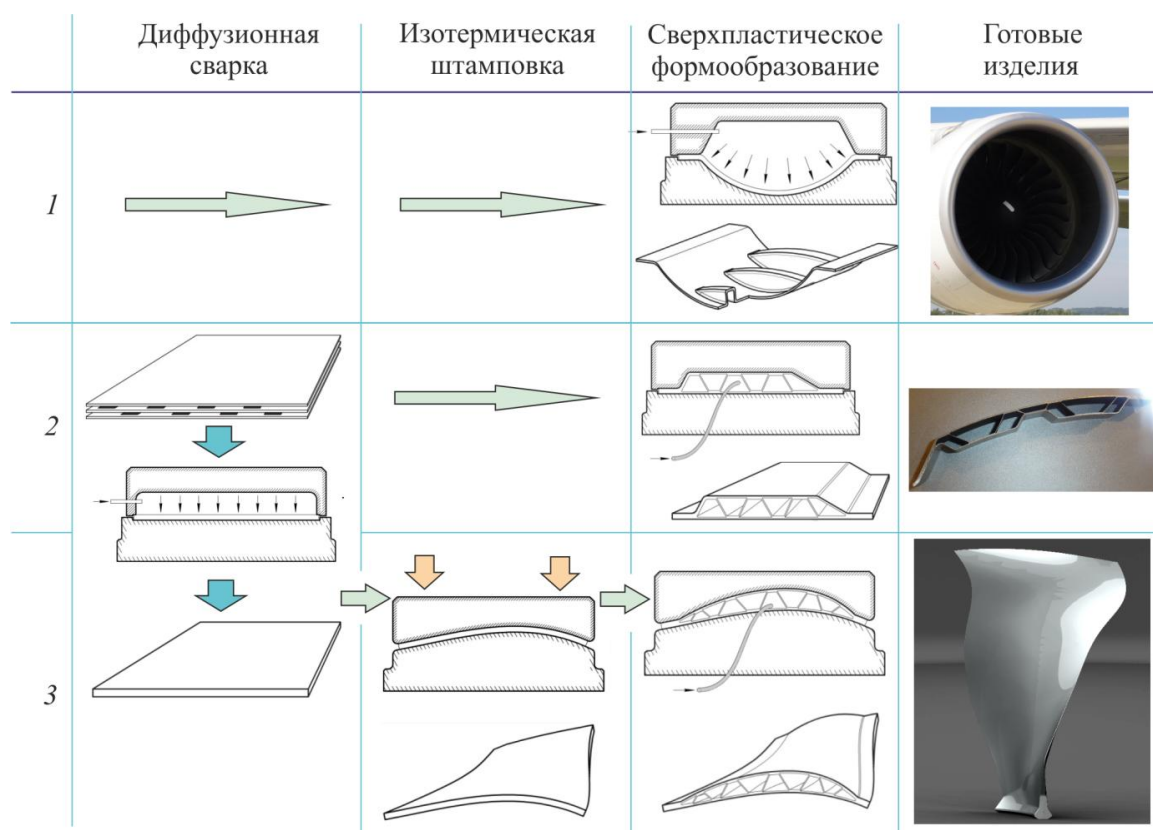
Схема применения операций диффузионной сварки, изотермической штамповки и сверхпластической формовки для различных деталей ГТД:
